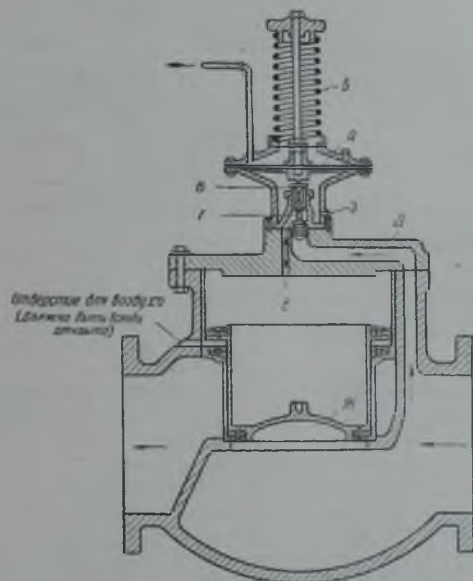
Высотный клапан (по материалам Golden-Anderson Valve Specialty Co.)
